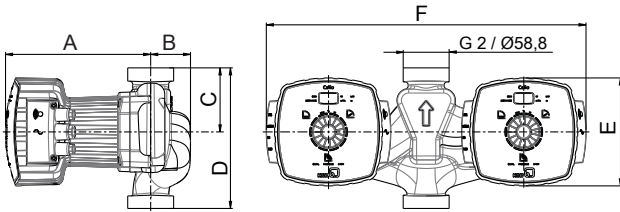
Pumpenaggregat mit Gewindeanschluss
